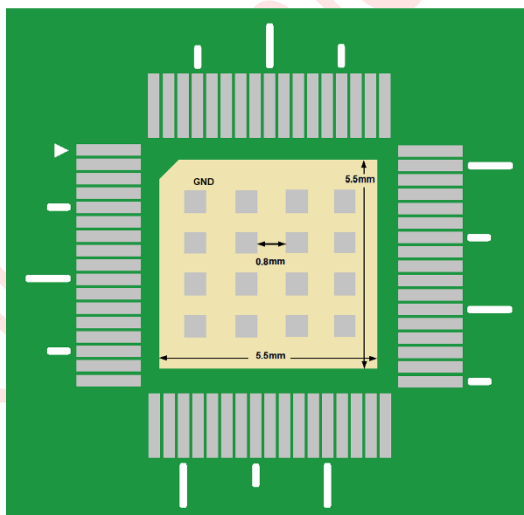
LT168B (QFN68) 焊盘与脚位图
